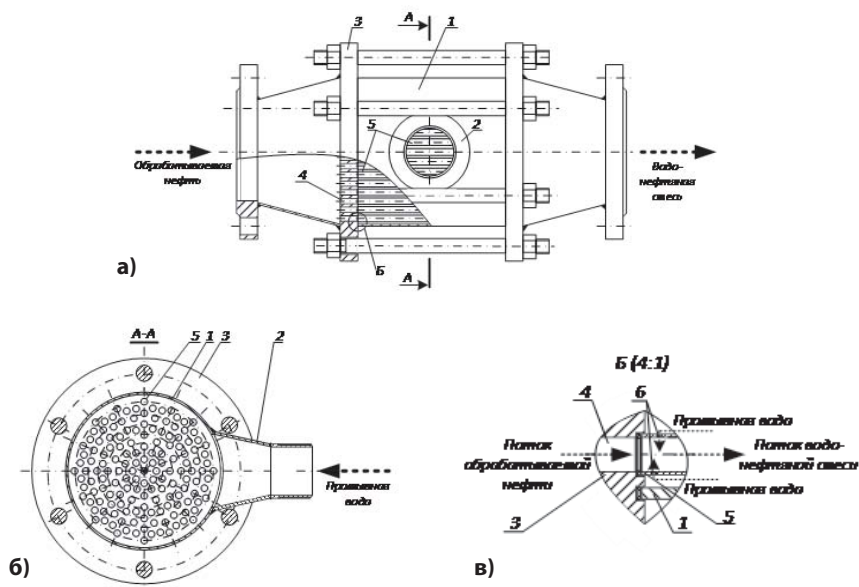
Струеинжеционный смеситель: а — общий вид; б — разрез; в — элемент; 1 — корпус; 2 — патрубок; 3 — крышки; 4 — отверстия; 5 — трубки; 6 — вводные отверстия
